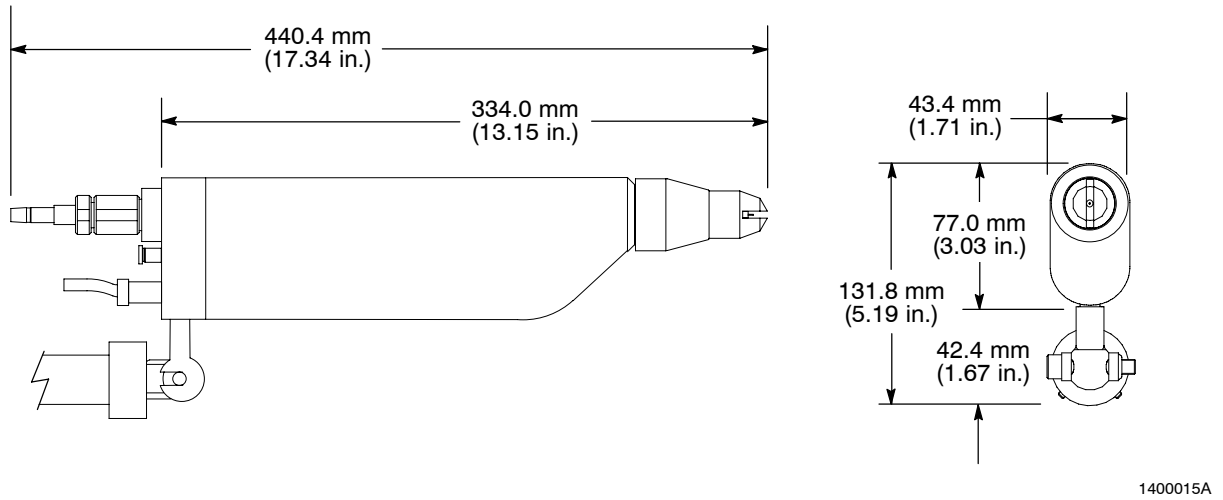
Dimensioni della pistola con montaggio su barra
